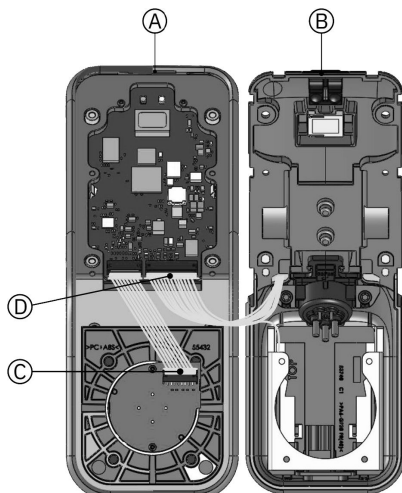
Separe la cubierta superior e inferior y desconecte el conector
